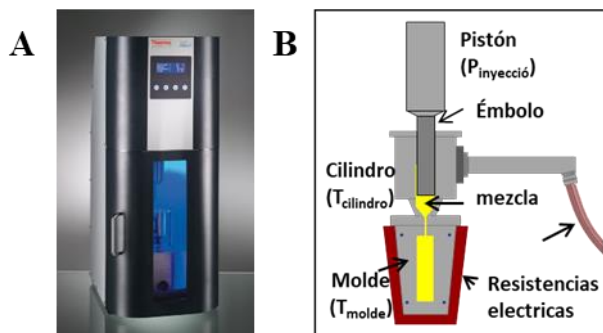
A: Inyectora MiniJet Piston Molding System II. B: Configuración de la inyectora.
